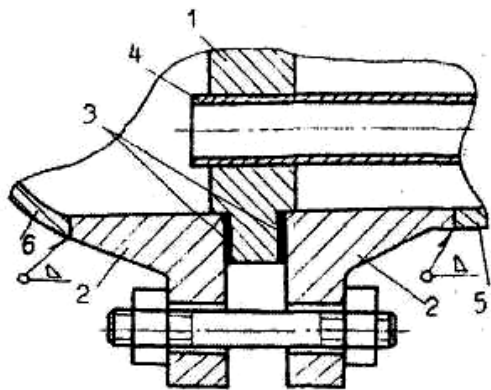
Узел крепления неподвижной трубной решетки: 1 – решетка трубная; 2 – фланец; 3 – площадка; 4 – трубка теплообменная; 5 – крышка
